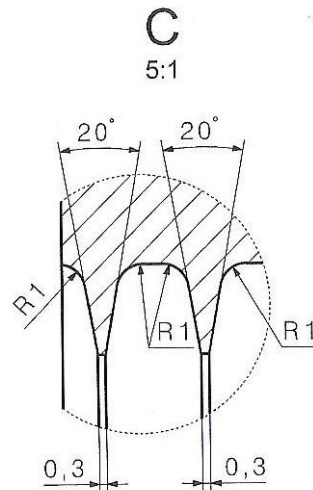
Detail sestavy – detail F – uložení labyrintového kroužku v rozváděcím kole proti břitům rotoru
